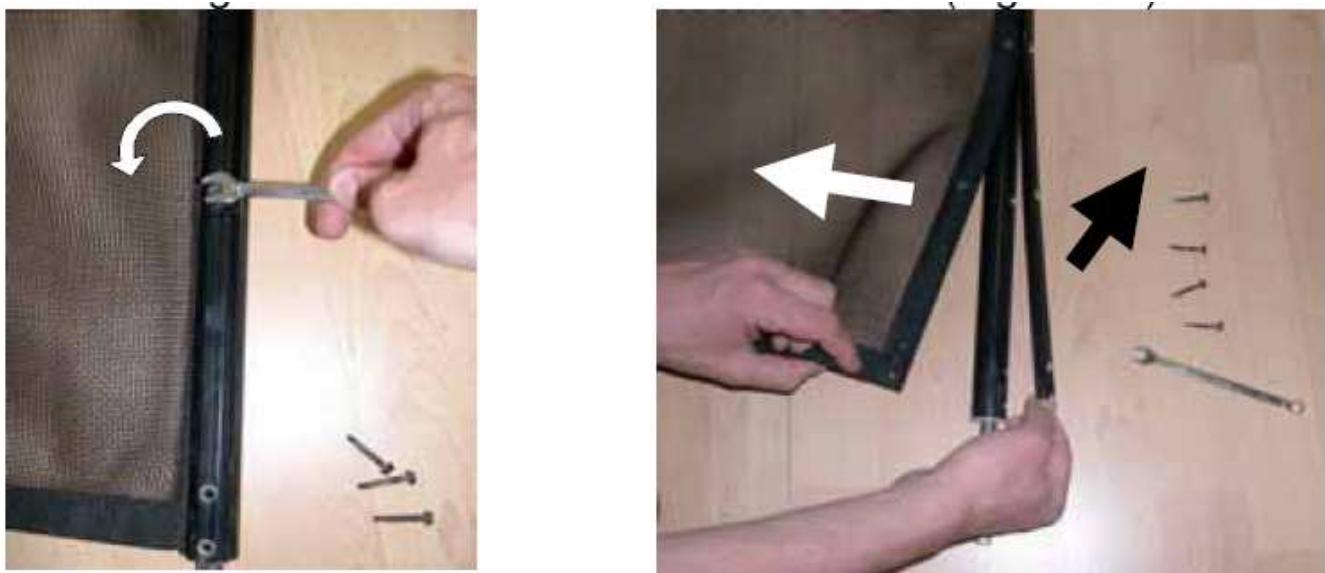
Svitare le 10 viti dall'asta della rete e staccare la rete
